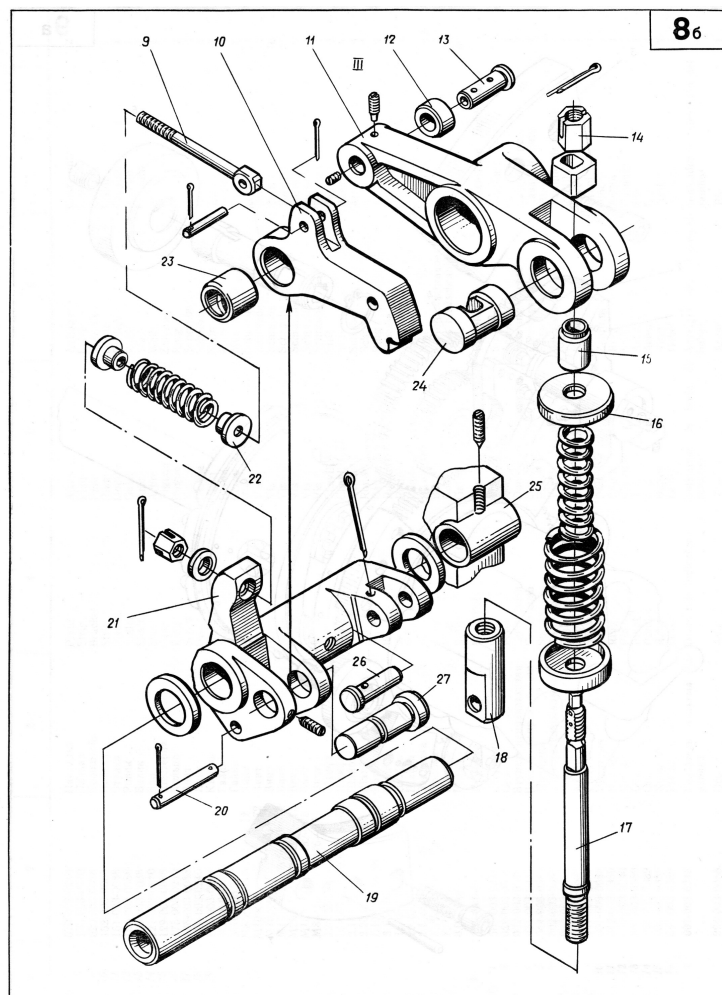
Схема з'єднання важеля з суміжними складальними одиницями вузла
